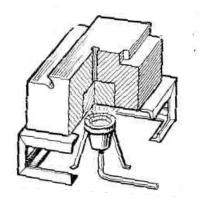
Приспособление для выпрессовки штамповой вставки
